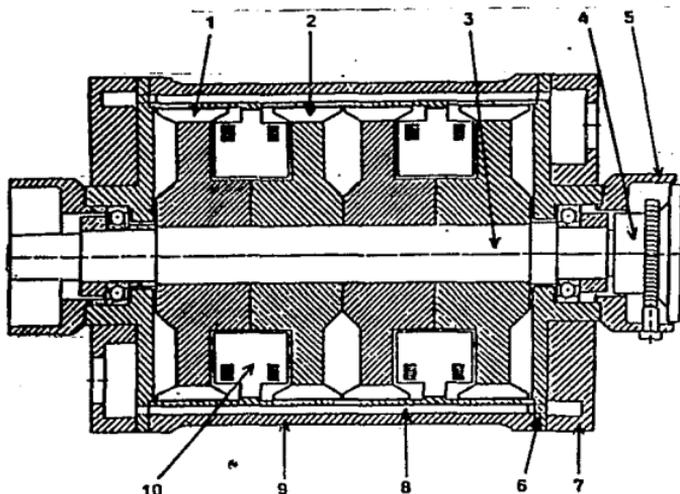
DINAMOMETRO DE ROTOR DOBLE.
